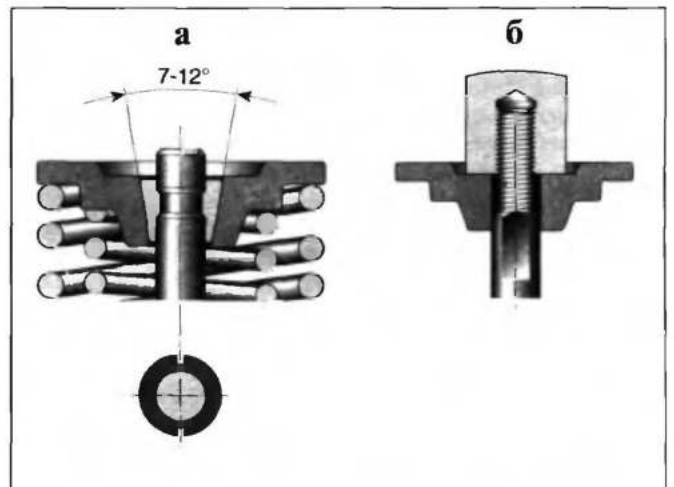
Крепление тарелки пружины на стержне клапана: а — с помощью сухарей; б — гайкой
